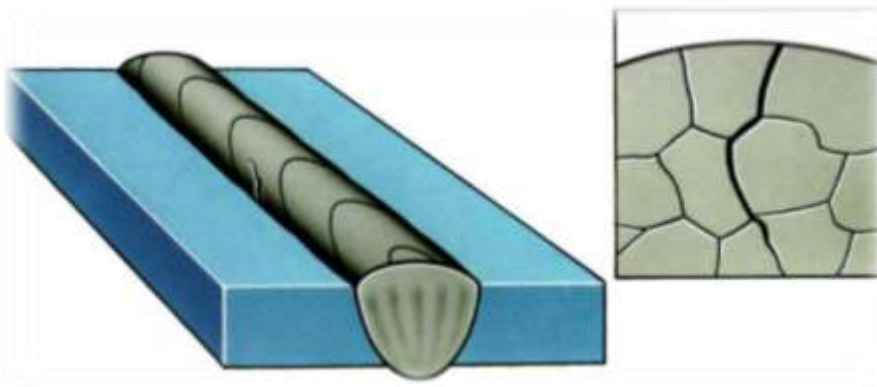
Дефекты сварного шва по типу трещин
